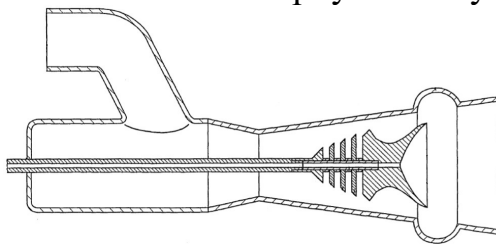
Змішувач зі змінними робочими елементами різного типорозміру (пат. № EP1280598A2, заявки № WO01/62373A1 та US2003/147303A1)
